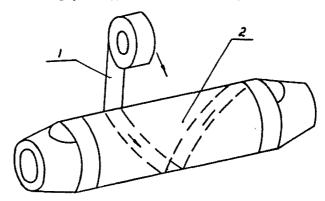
Закрепление защитного слоя на корпусе пометинительного завима с помощью изоляционной ленты:
